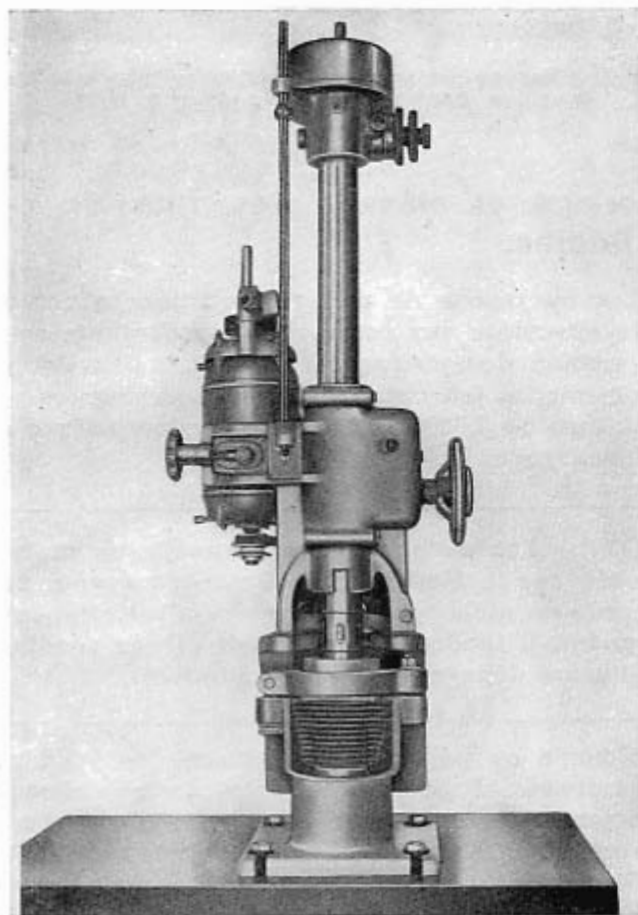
Alésage d'un cylindre sur aléreuse portable M. 111, au moyen de l'outil A. 60000.
